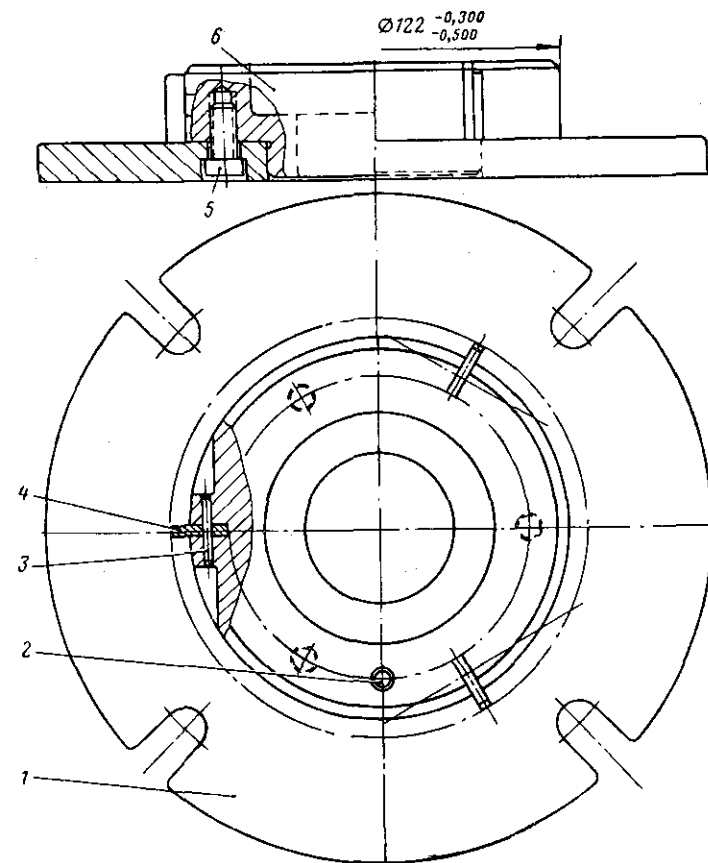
Приспособление 63509/715 для сборки узла станка:
